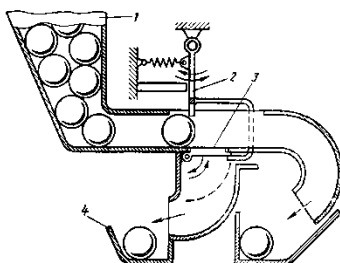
Автоматический прибор для сортировки и подачи подшипниковых шариков на конвейер
